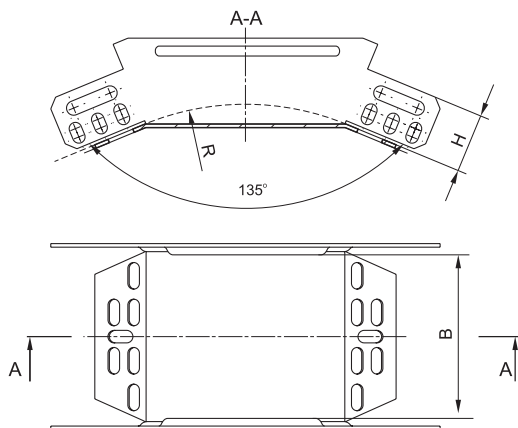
Поворот 45° вертикальный внешний. Размеры для размещения кабеля /
